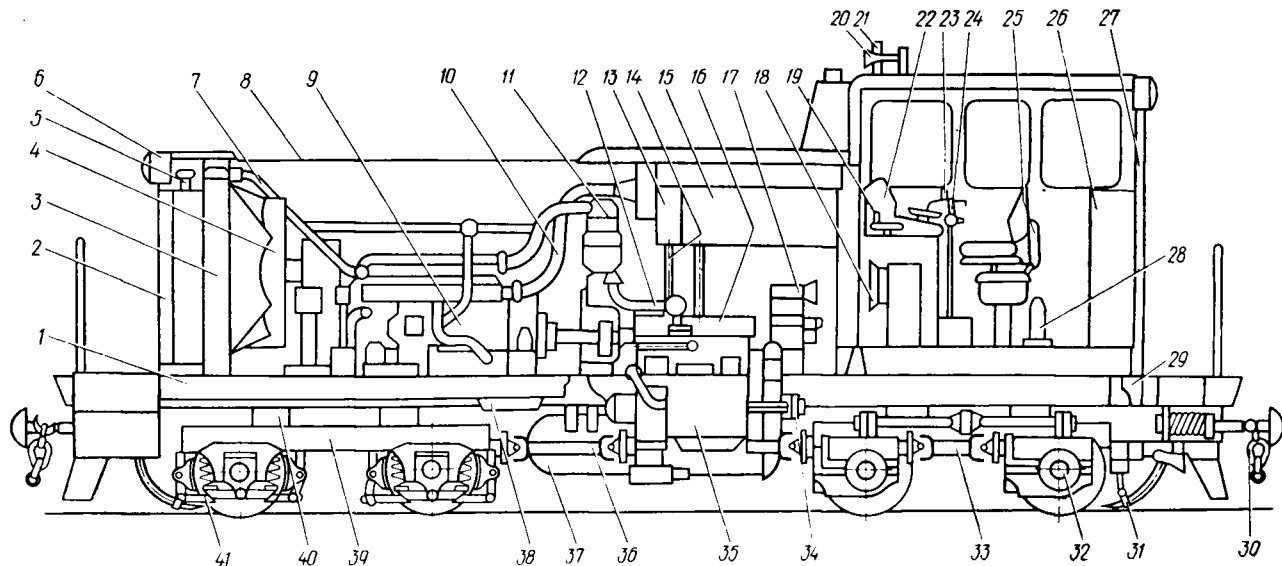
Продольный разрез тепловоза ТУ7 (схема):
